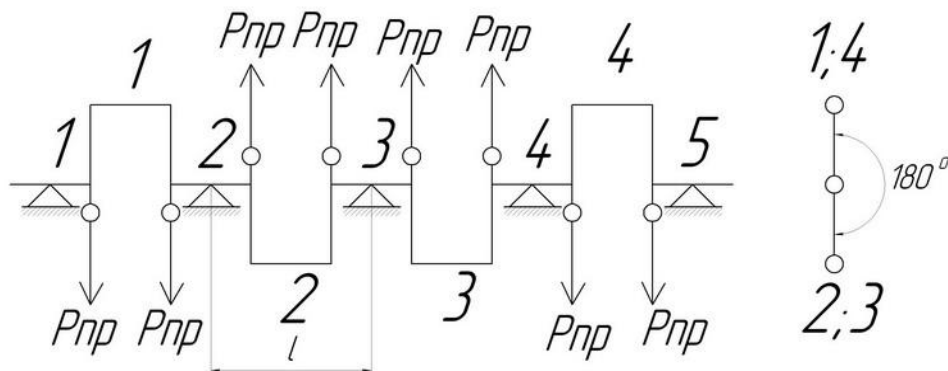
Порядок работы двигателя и схема коленчатого вала.
